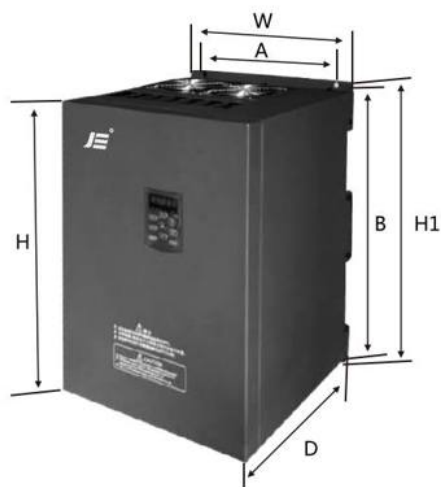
JL910系列 钣金结构外型尺寸及安装尺寸示意图
